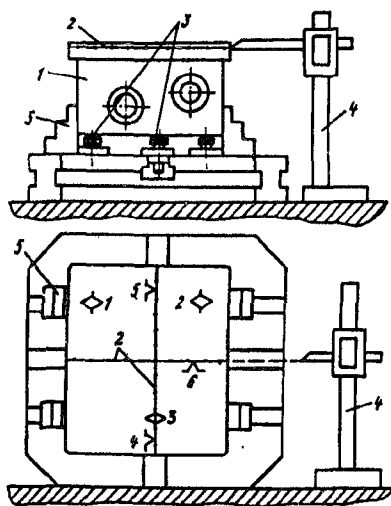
Схема базирования заготовки в приспособлении-спутнике по разметке
